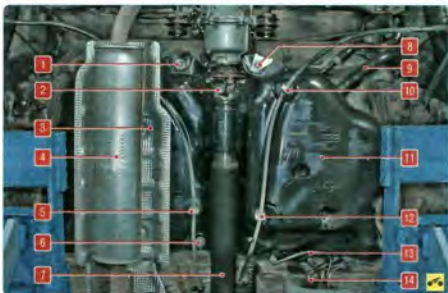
Топливный бак полноприводного автомобиля: 1 – левый болт заднего крепления бака; 2 – задний шарнир карданного вала; 3 – термозащит; 4, 10, 12 – держатели тросов стояночного тормоза; 5 – дополнительный глушитель; 6 – передний болт крепления бака; 7 – карданый вал; 8 – правый болт заднего крепления бака; 9 – труба наливной горловины; 11 – топливный бак; 13 – трубопровод подачи топлива; 14 – шланг отвода паров топлива к адсорберу
